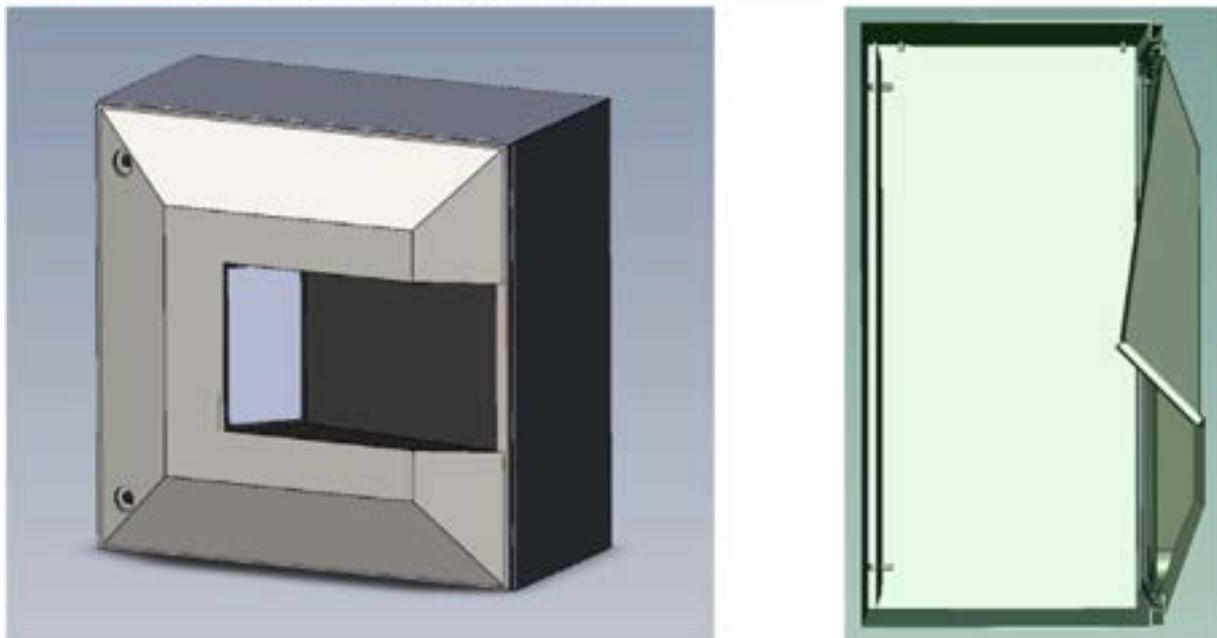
Betrieb im Außengehäuse für Tunnelanwendung
